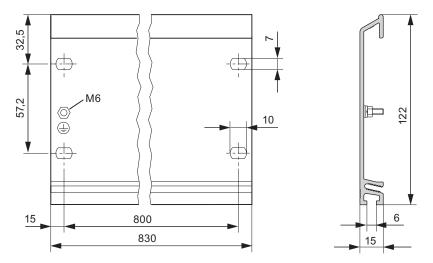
Plan d'encombrement du profilé support de longueur standard 830 mm
